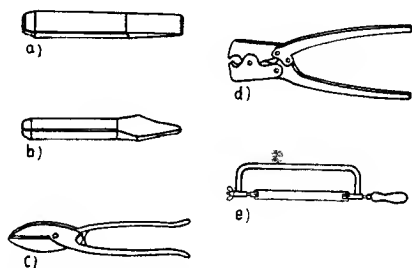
Trennwerkzeuge; Flachmeißel (a), Kreuzmeißel (b), Handblechschere (c), Hebelvorschneider (d) und Handbügelsäge (e)
